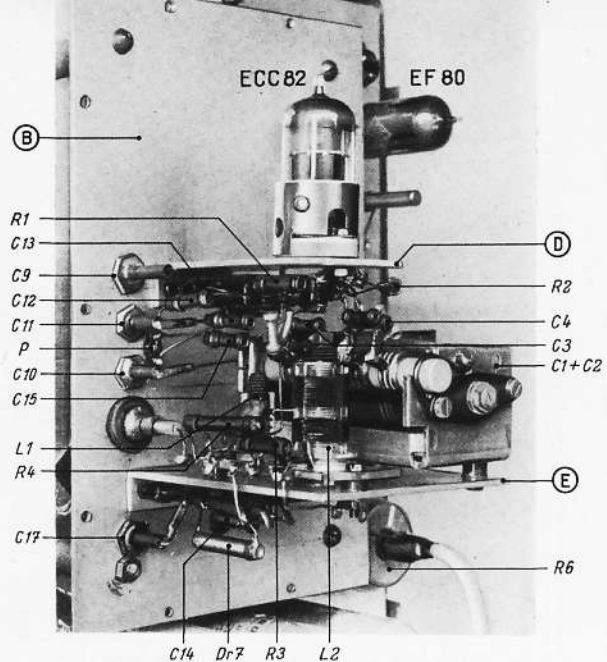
Innenaufbau des Generatorbauteiles. B = Grundplatte, D = Tragwinkel für die Schwingröhre, E = für die Schwingkreise
